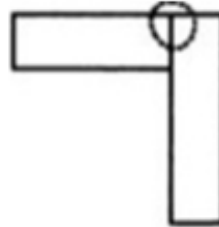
Représentation de l'assemblage des tôles et de la soudure
